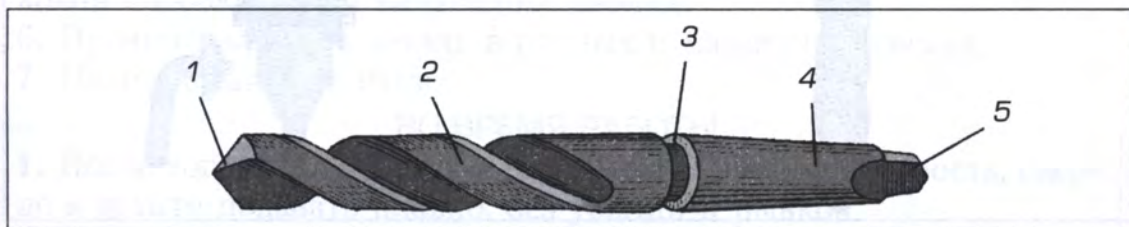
Сверло для сверлильного станка с коническим хвостовиком:
